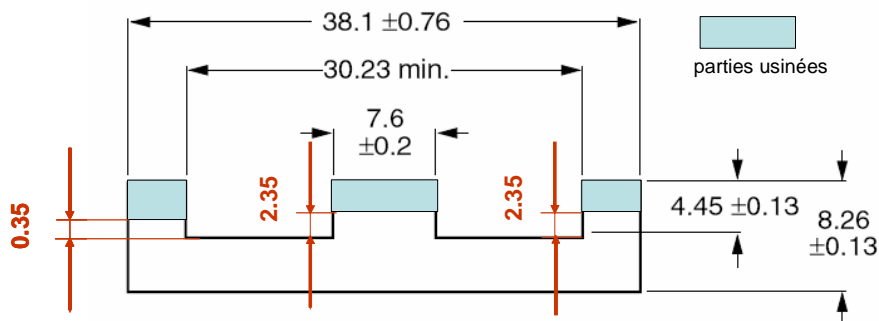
Usinage du noyau magnétique de prototype A (E38/8/25)
